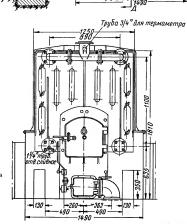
Габаритные размеры модернизированного котла "Универсал"
